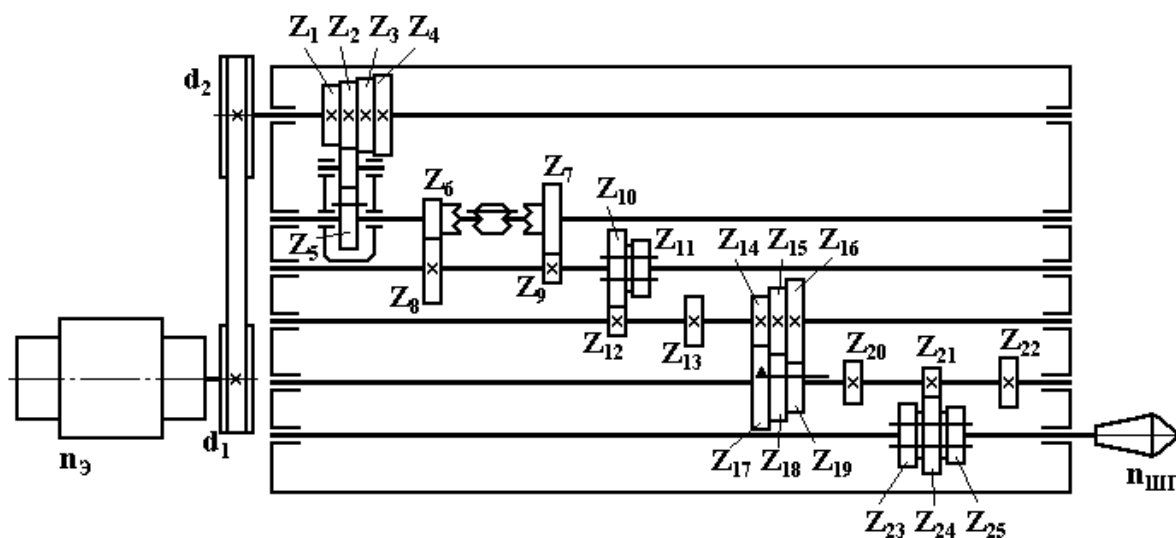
Кинематическая цепь главного движения условного станка (вариант № 3)
